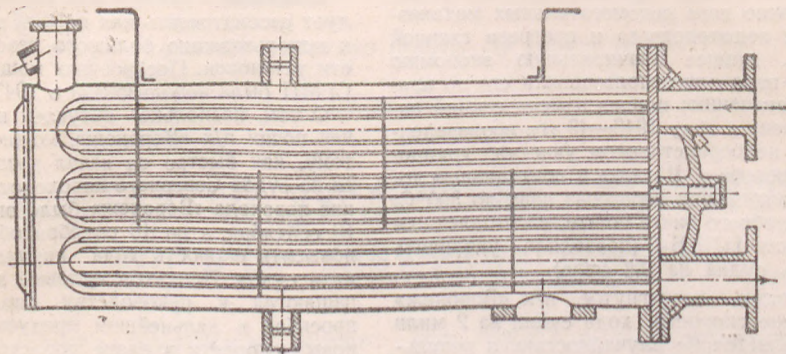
Водоподогреватель с толстостенным сварным корпусом
